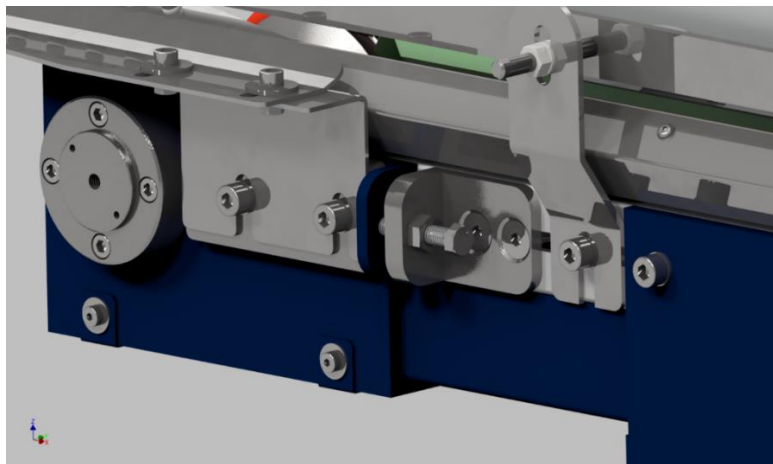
Vizualizace konstrukce – pohled od přejímacích kladek
